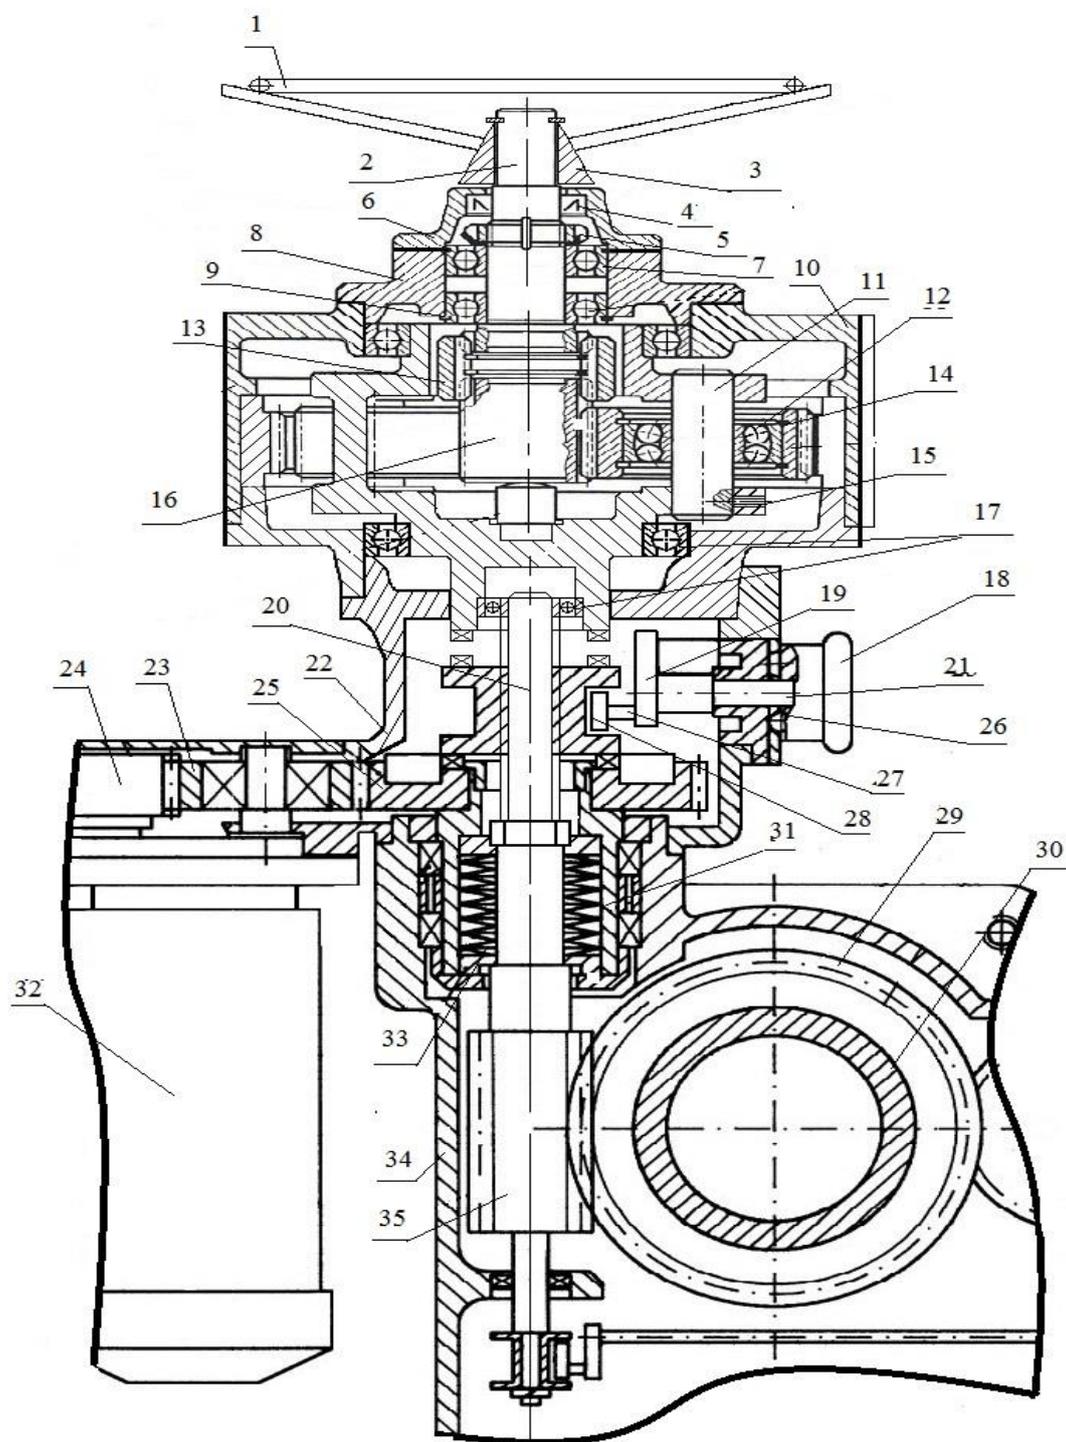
Схема электропривода с ручным дублером на основе планетарной передачи
